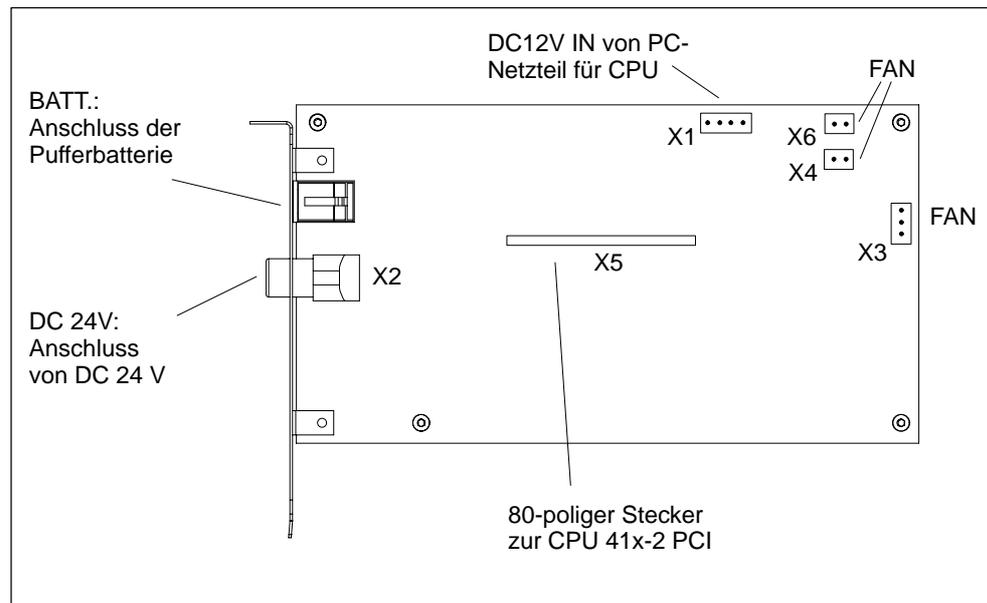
Lage der Anschlussstecker auf dem PS Extension Board
